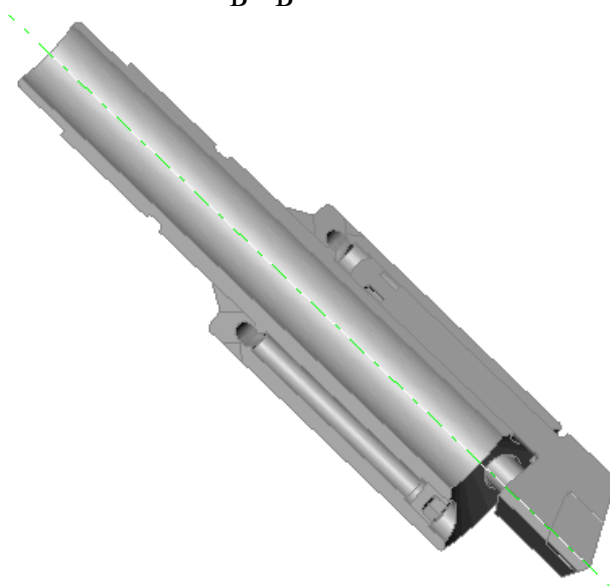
Конструкція адаптивного свердла з рухомими лезами.
